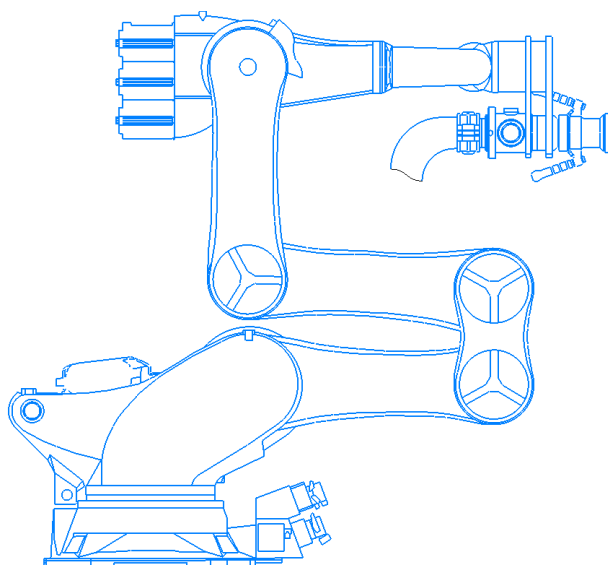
Модернизированный робот-манипулятор Kuka KR 340 R3330
